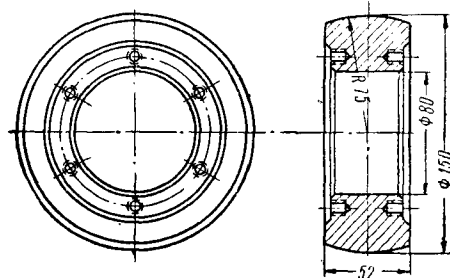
Схемы конструкций роликов для накатывания осей и других деталей
